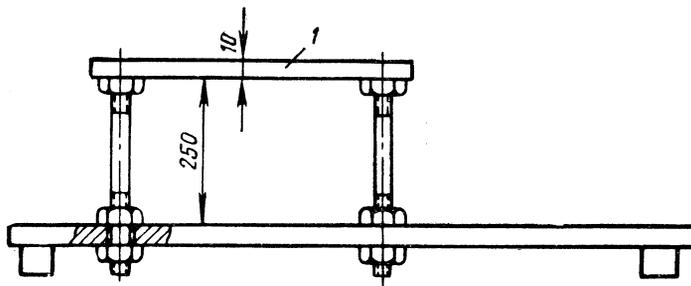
Приспособление для разборки-сборки стартеров и прерывателей-распределителей
